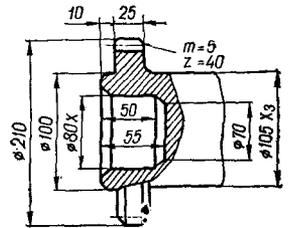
Размеры зубчатой полумуфты тихоходного вала редуктора РЦД-400.
